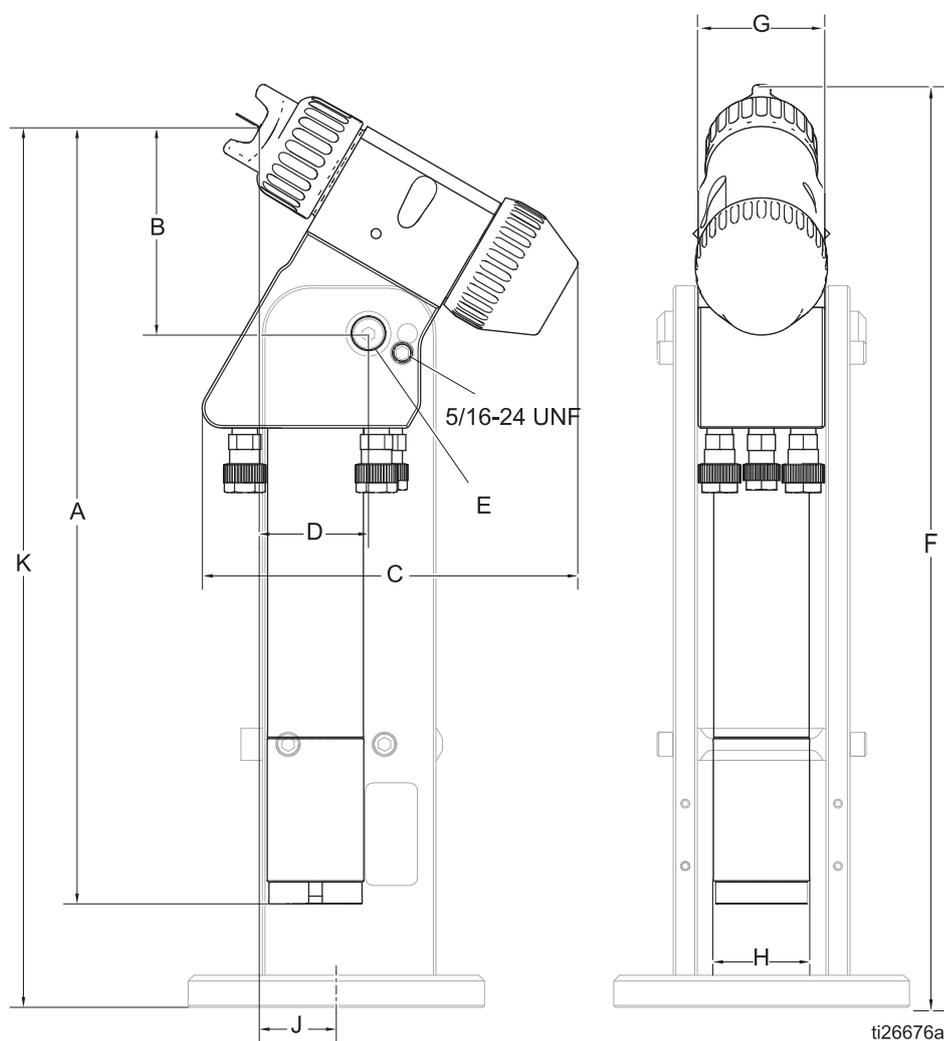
Pistola per montaggio posteriore - Dimensioni
